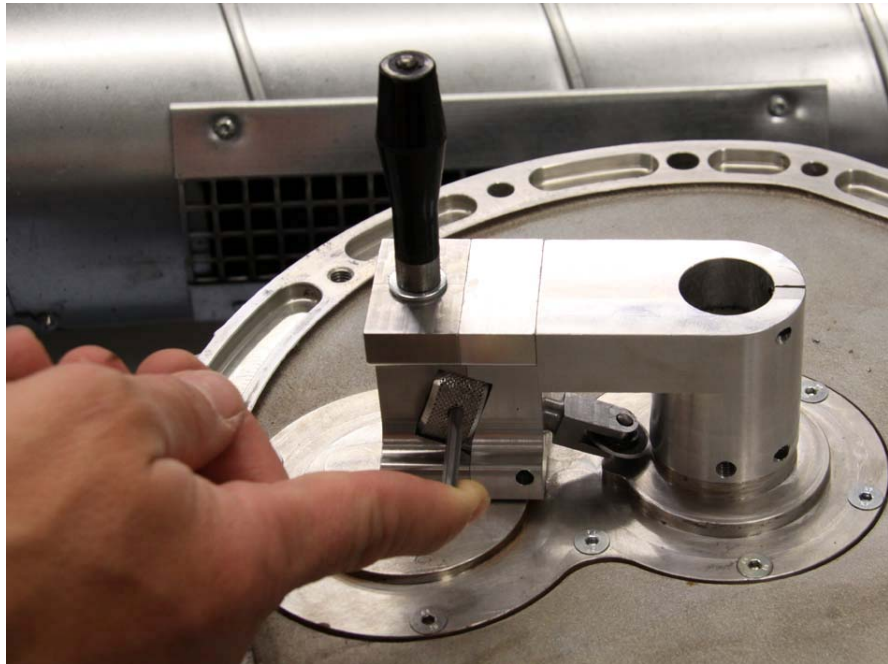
Das Schneidwerkzeug am Einstellrad zustellen
